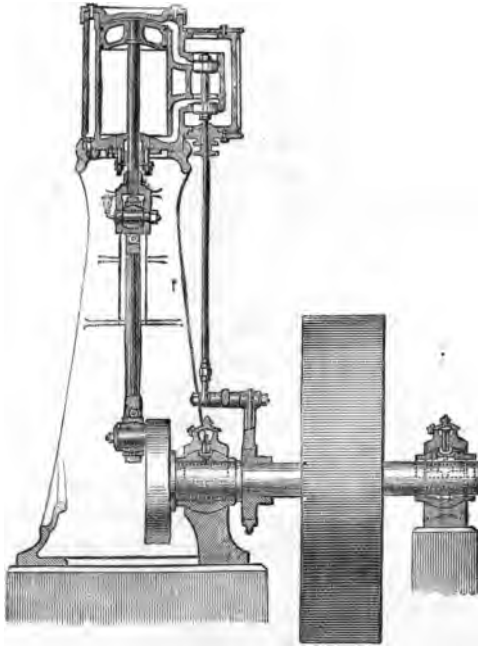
Machine à vapeur fixe verticale. — Coupe.
